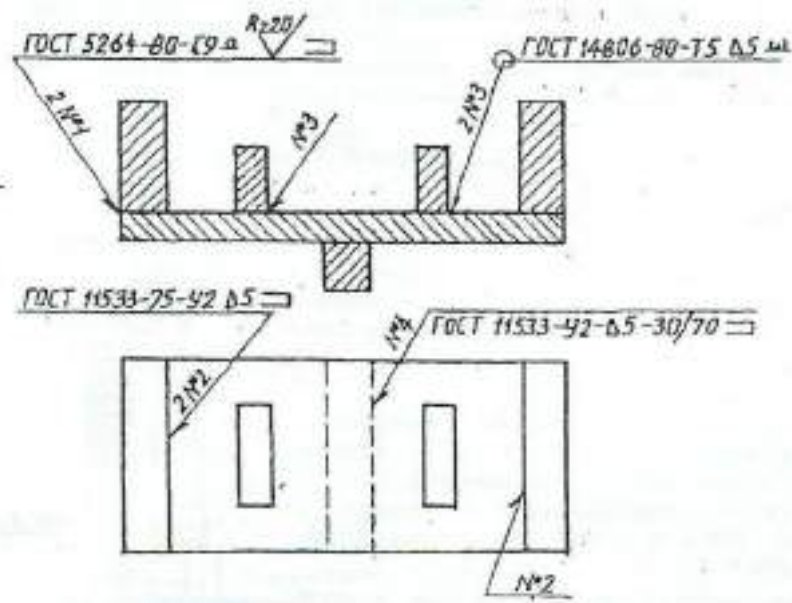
Условное обозначение сварных соединений
